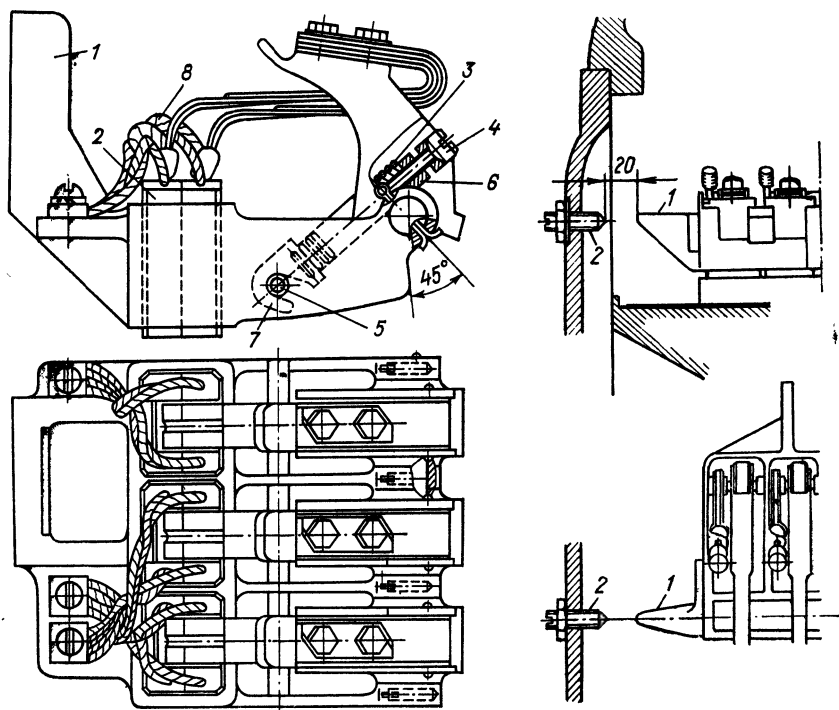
Щеткодержатель двигателя НБ-418К6
